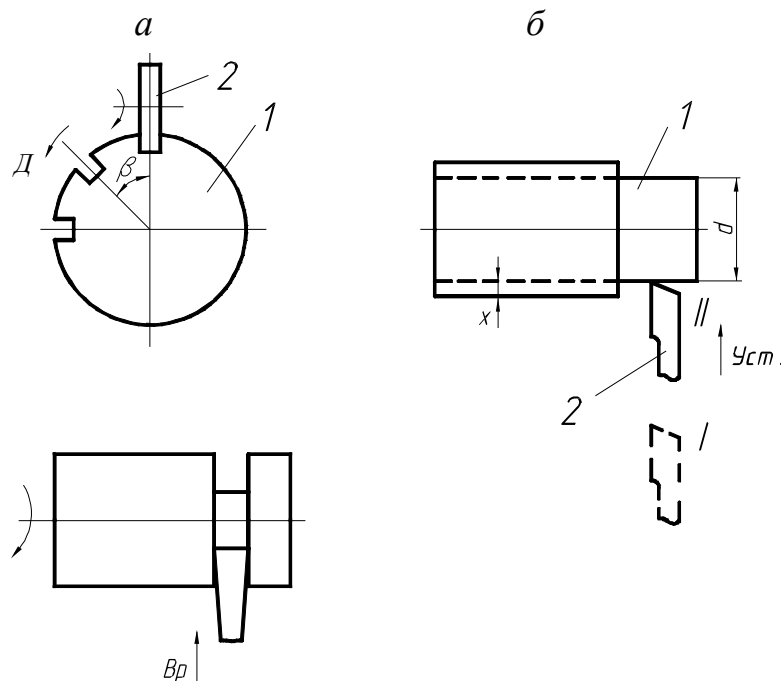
Схемы выполнения движений на станках: а – движение деления (Δ); б – установочное движение ($Уст$); в – движение врезания ($Вр$).
